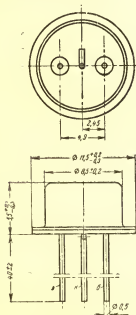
Габаритный чертеж транзисторов П401—П403А.
